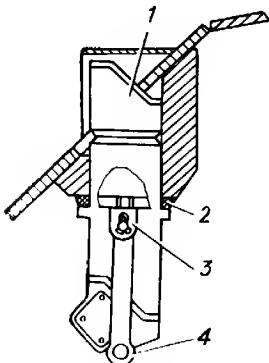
Установка бокового прибора наблюдения ТНПО-115:
